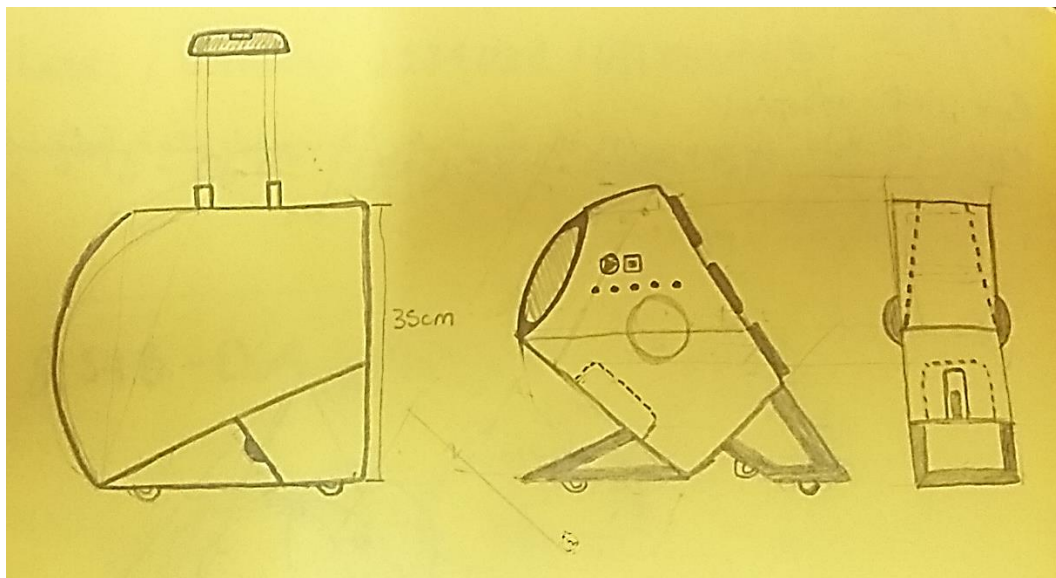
Fuente: Elaboración propia. Esquema constructivo para modelo de estudio.
